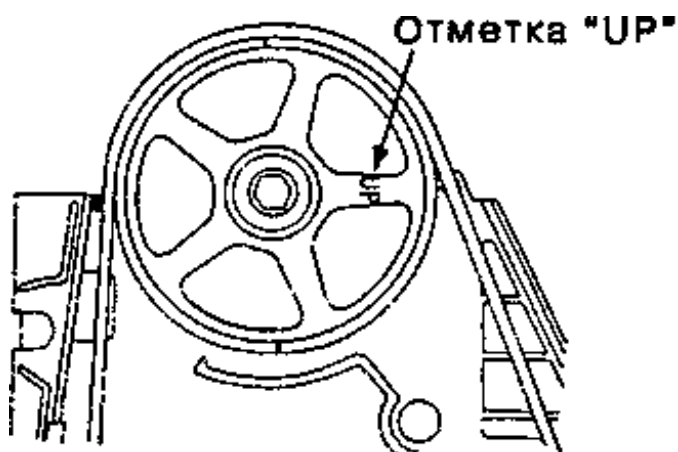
Положение шкива распредвала при регулировке клапанов второго цилиндра
